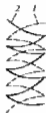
Движение горелки и проволоки при сварке стали толщиной более 3 мм в нижнем положении: 1 — движение проволоки; 2 — движение горелки
